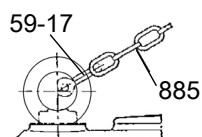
Befestigung der Kette mit Schäkel an der Ringschraube
